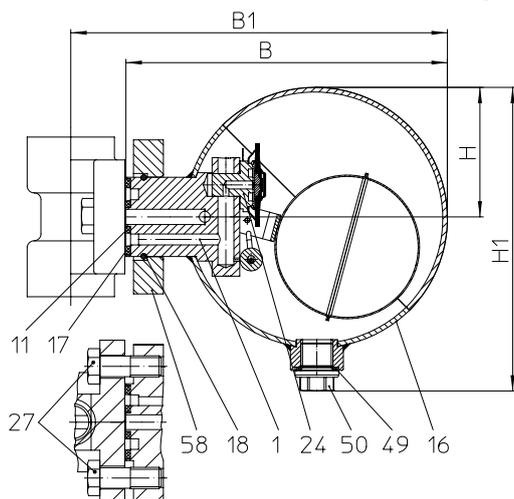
Universal-Flansch mit 2 x 3/8" UNC-Gewinde
